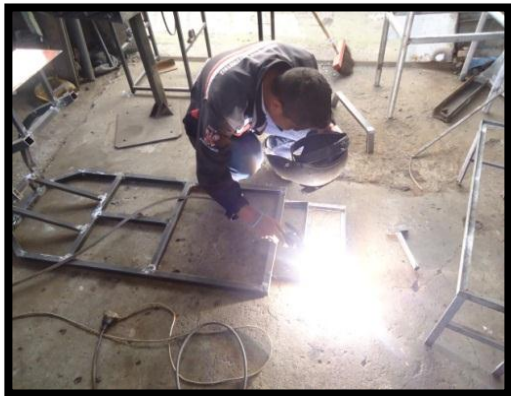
26 – Soldadura base del C.P.U.
